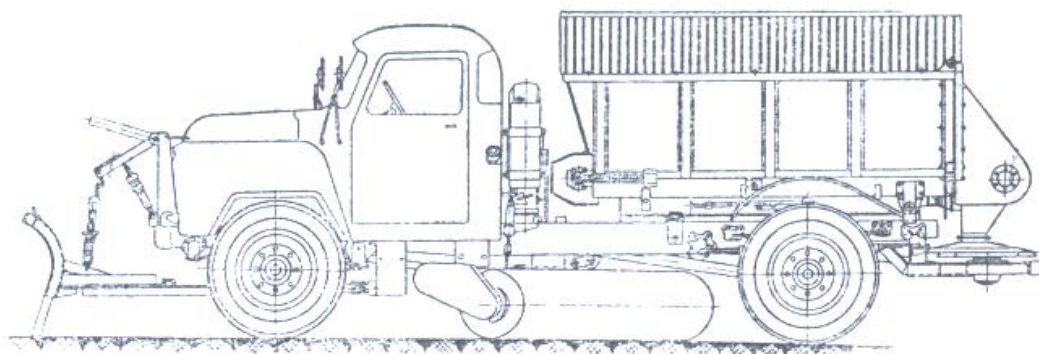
Общий вид пескоразбрасывателя ПР–53
